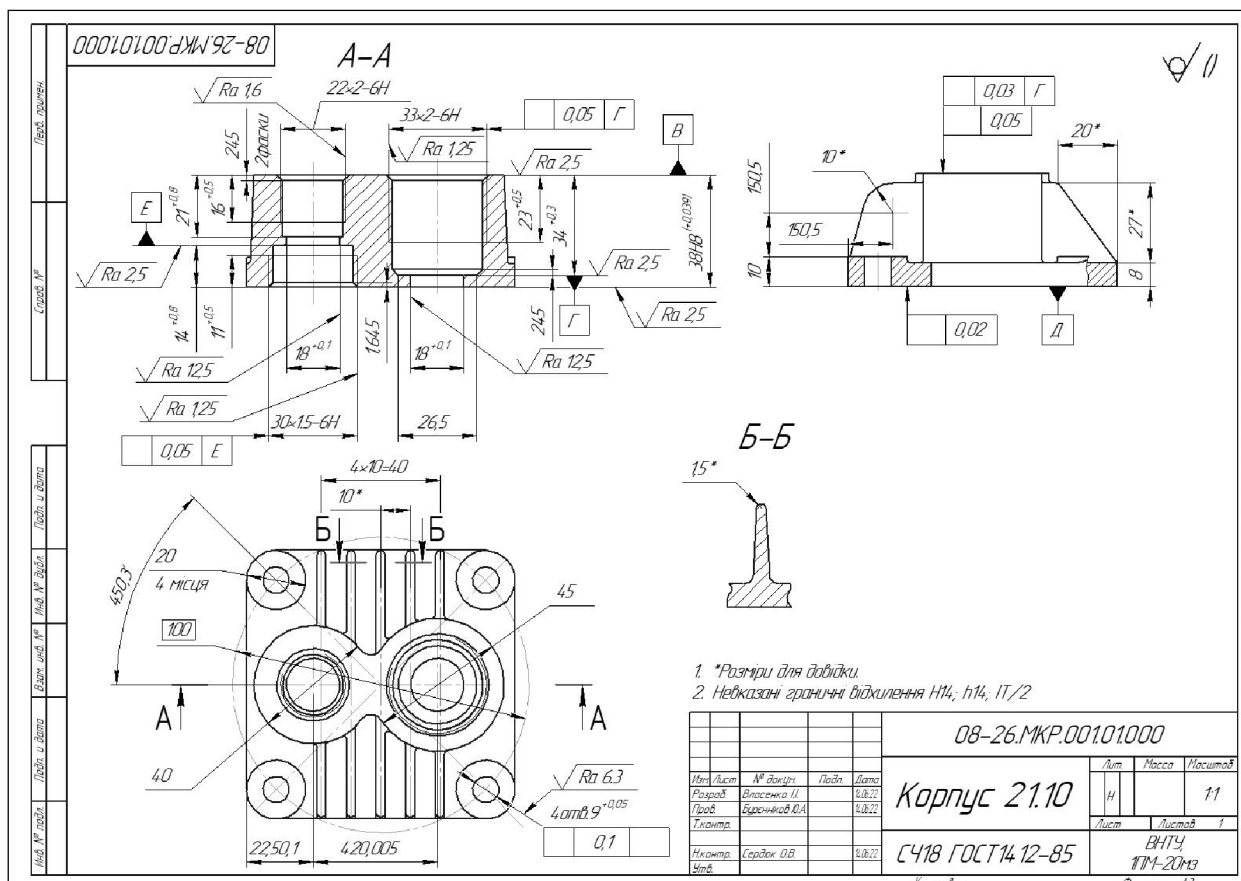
Креслення деталі «Корпус 21.10»
